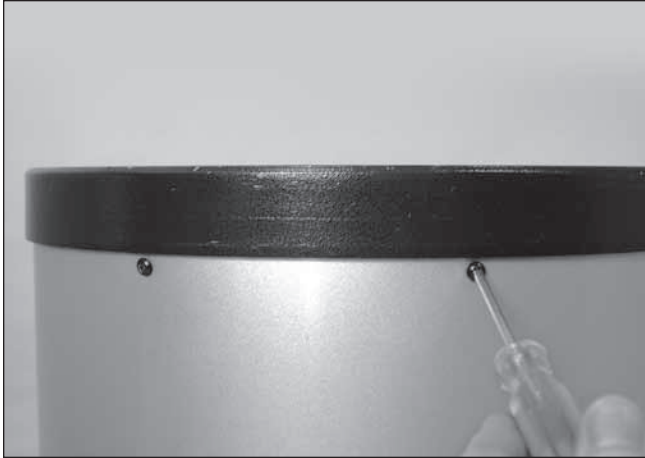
Lösen Sie zum Entfernen des hinteren Endrings die acht Schrauben, mit denen er am Optiktrohr befestigt ist.
